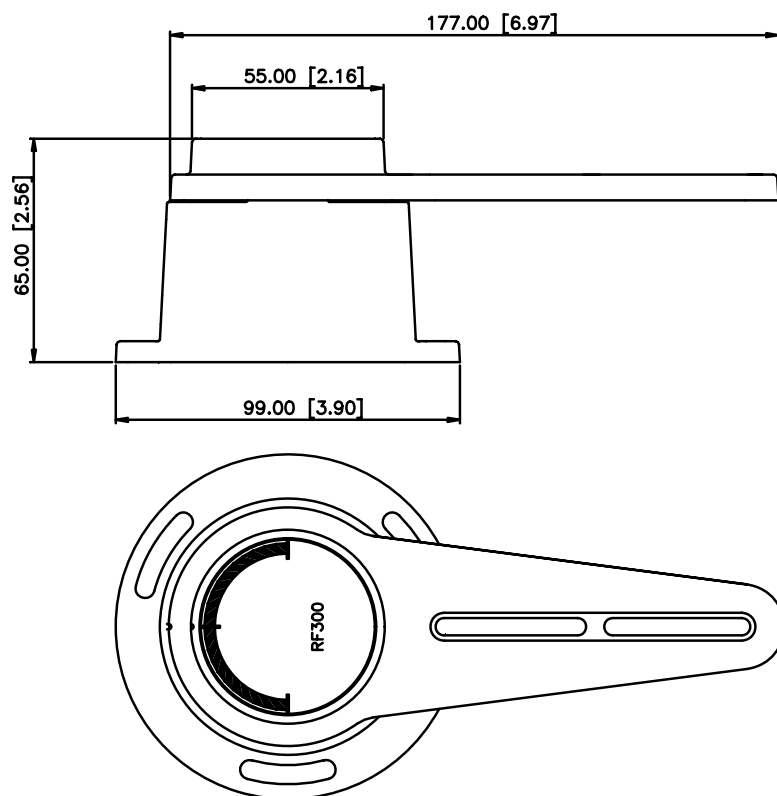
Emetteur d'Angle de Barre RF300 - Dimensions
